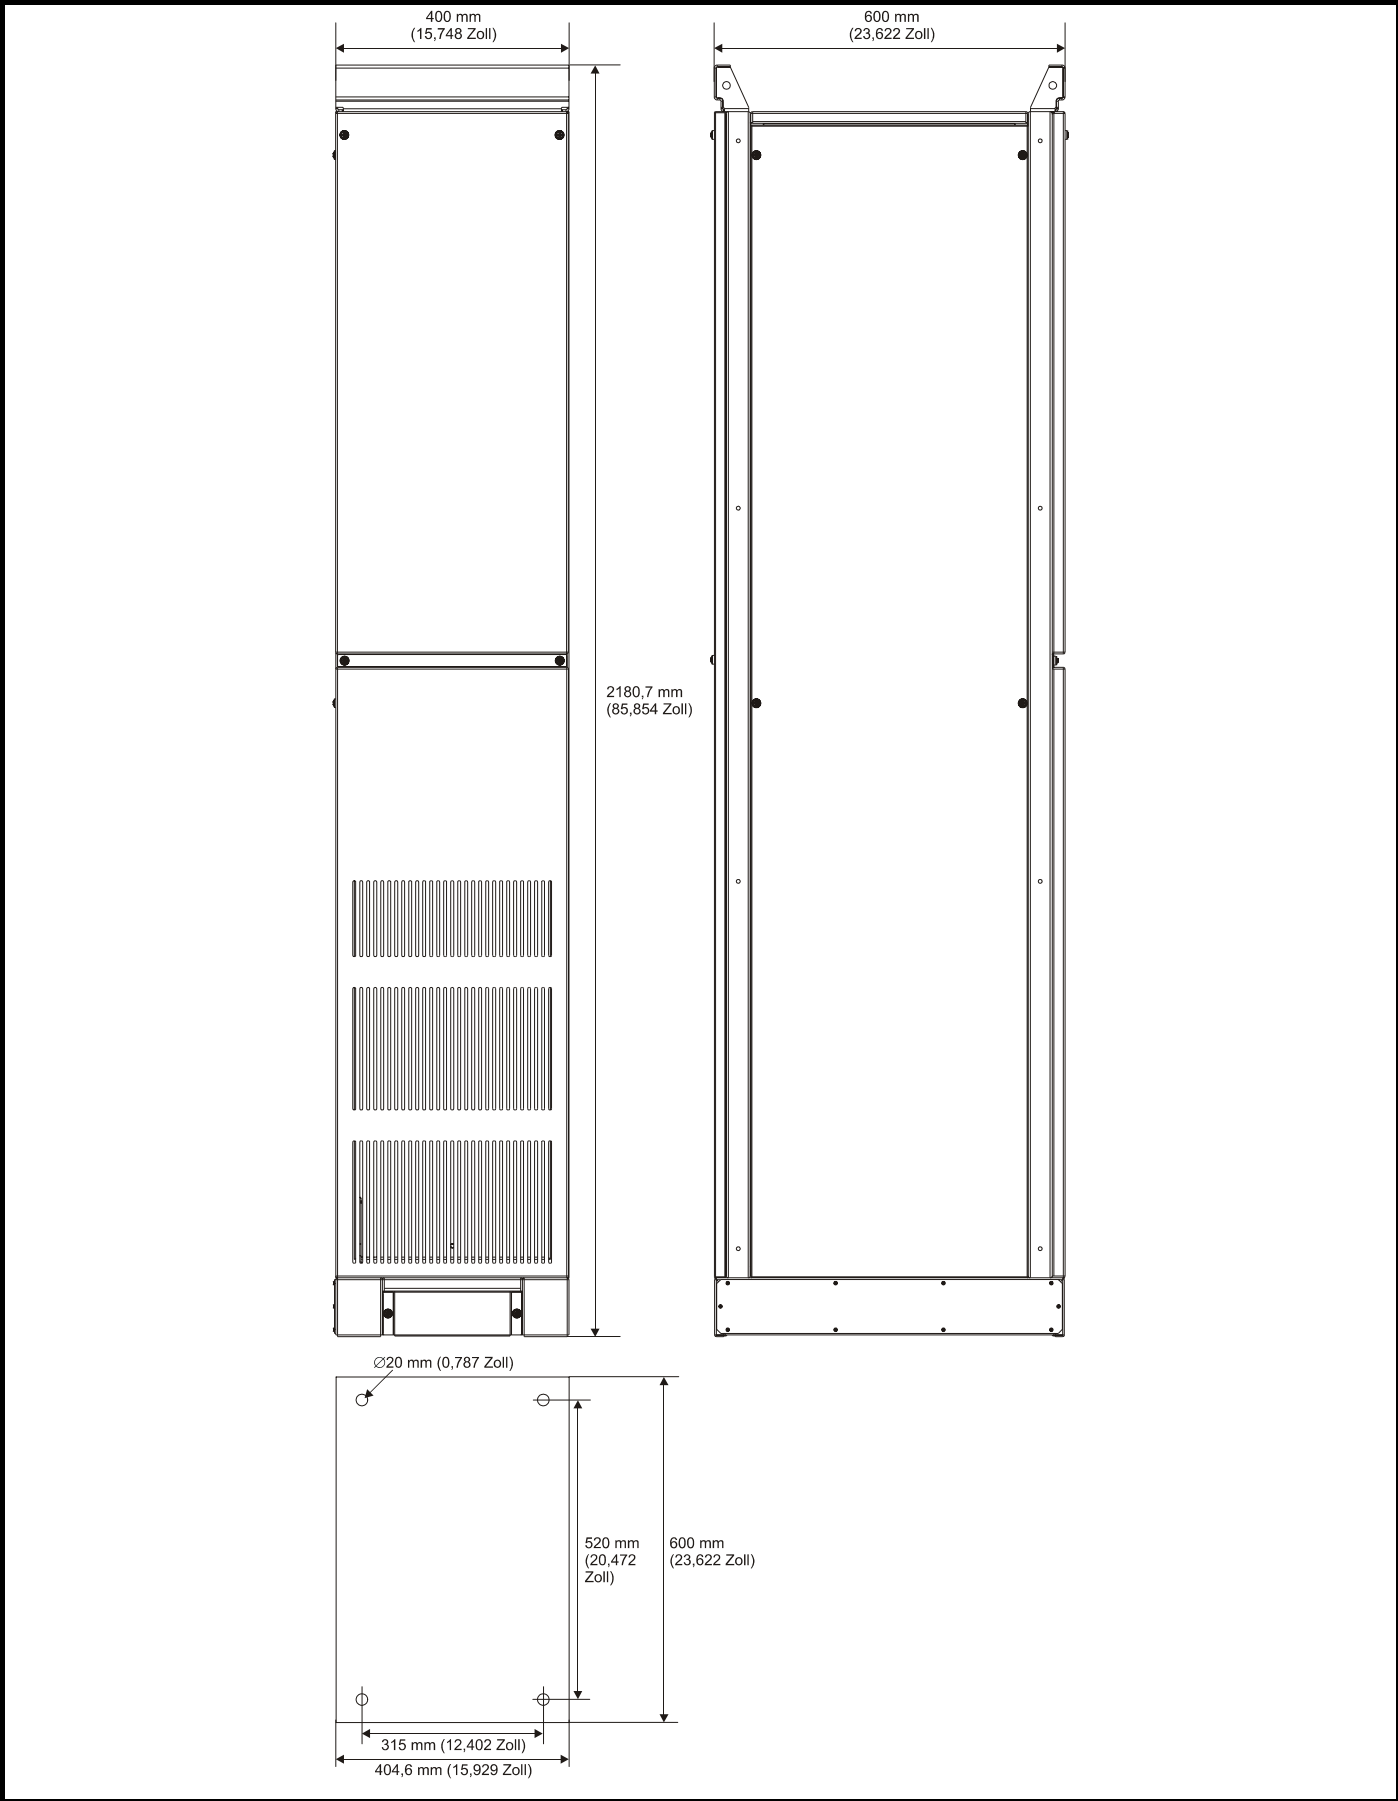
Abmessungen des Umrichterschrank Baugröße 8
